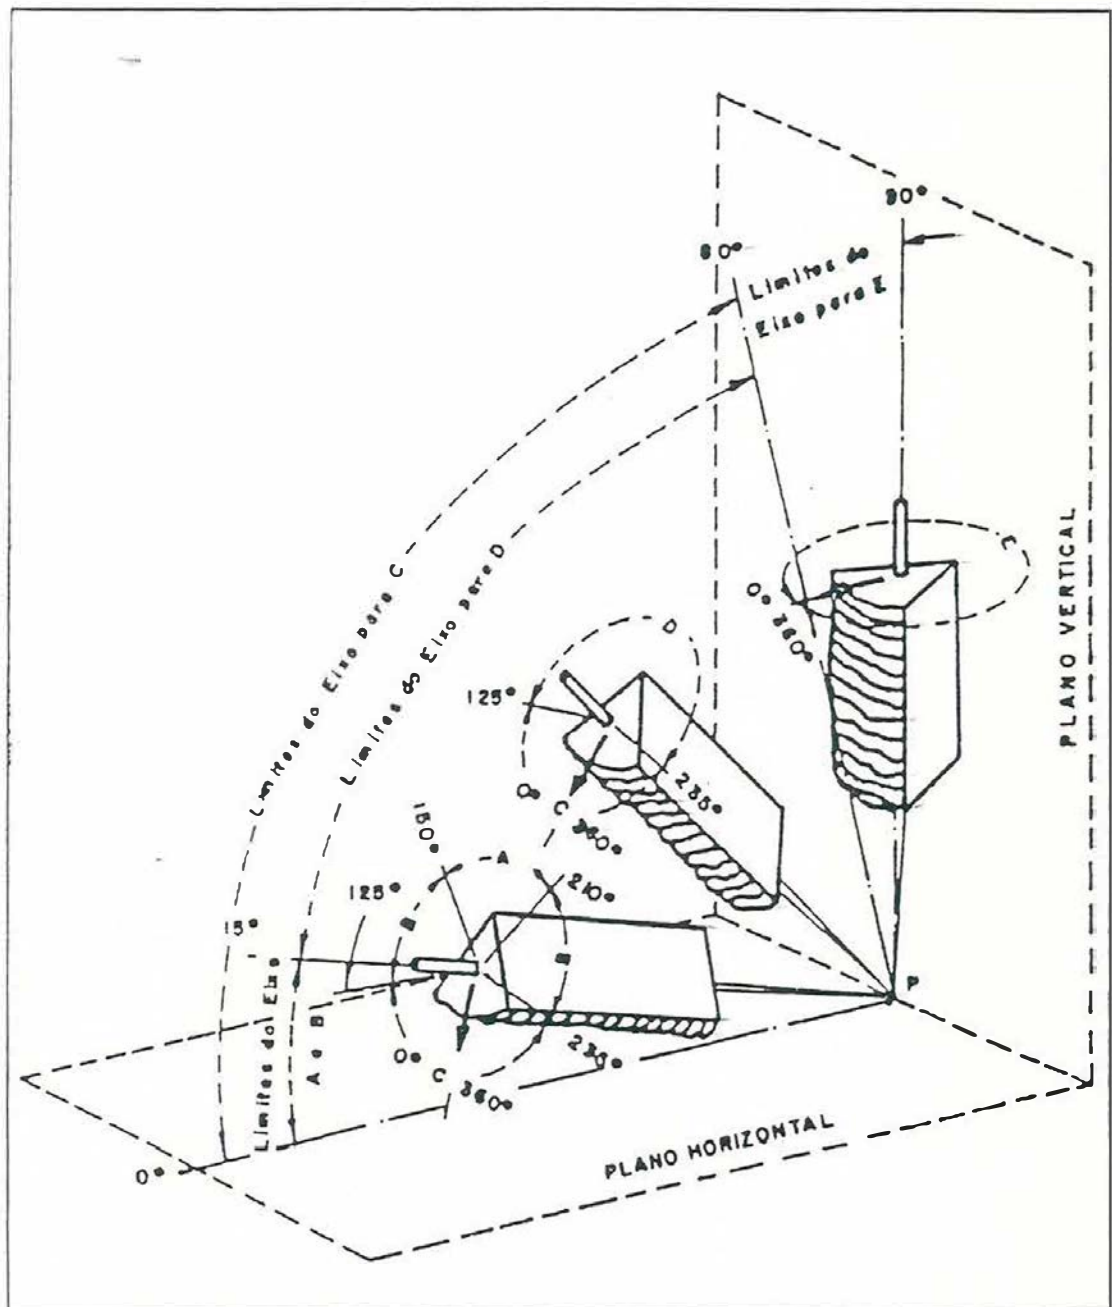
Tabulación de las posiciones de soldadura en ángulo.
